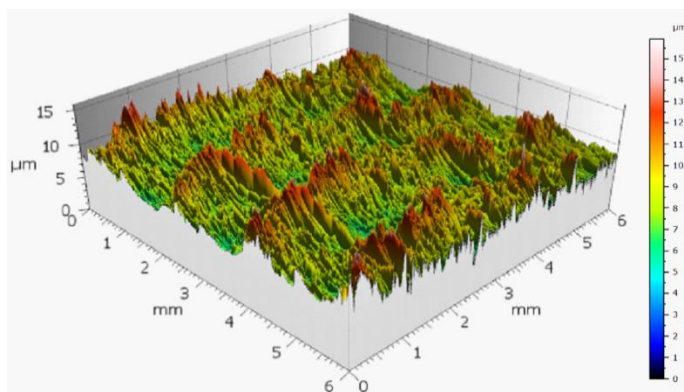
Топографія обробленої поверхні після фрикційної обробки інструментом з різнонаправленими пазами
